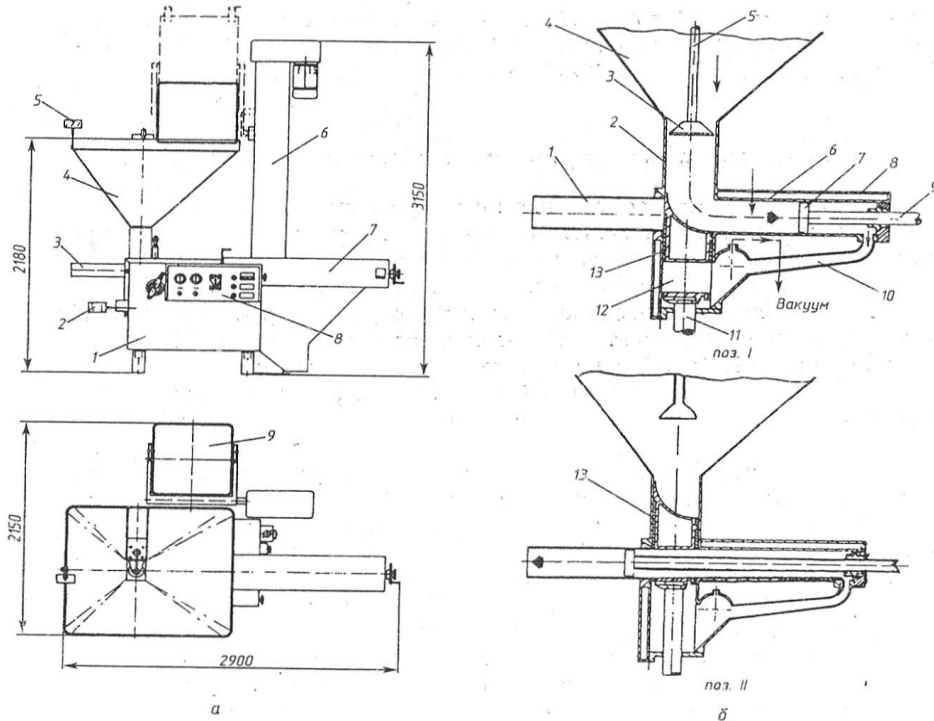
Поршневий наповнювач-дозатор з пневматичним приводом фірми "Сіа":
